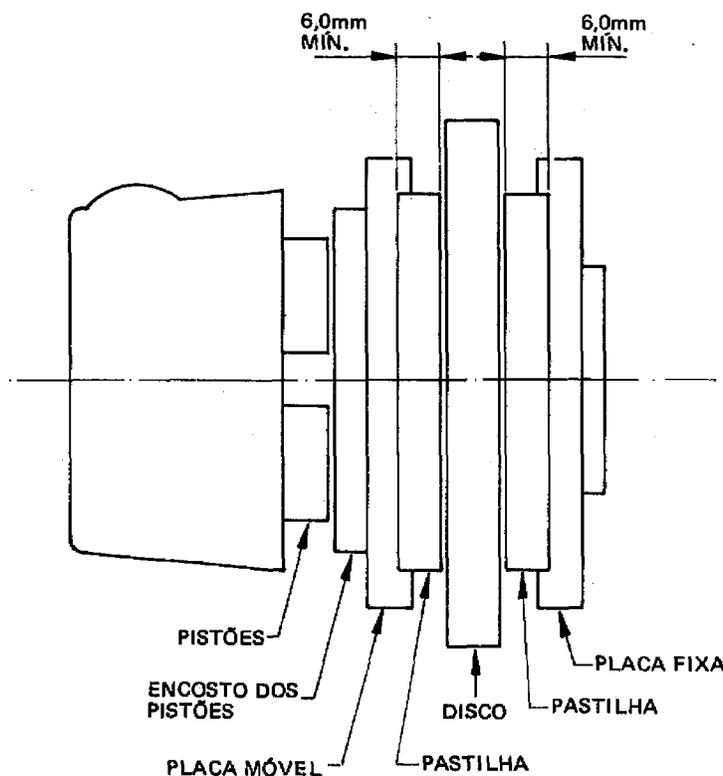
Inspeção e Limites de Desgastes das Pastilhas de Freio
